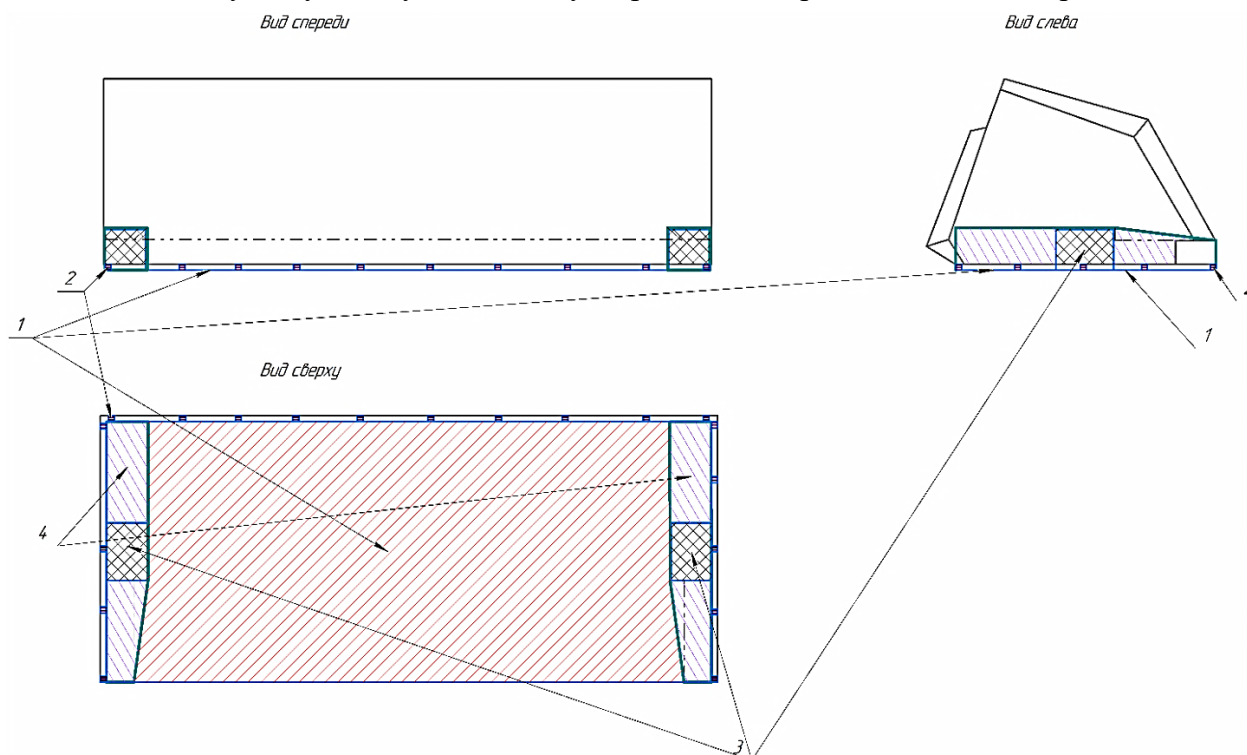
Схема ковша 1 плита с продольными выступами для очистки поверхности от ледяных образований; 2 виброизоляторы; 3 Вибромоторы; 4 защитный короб
